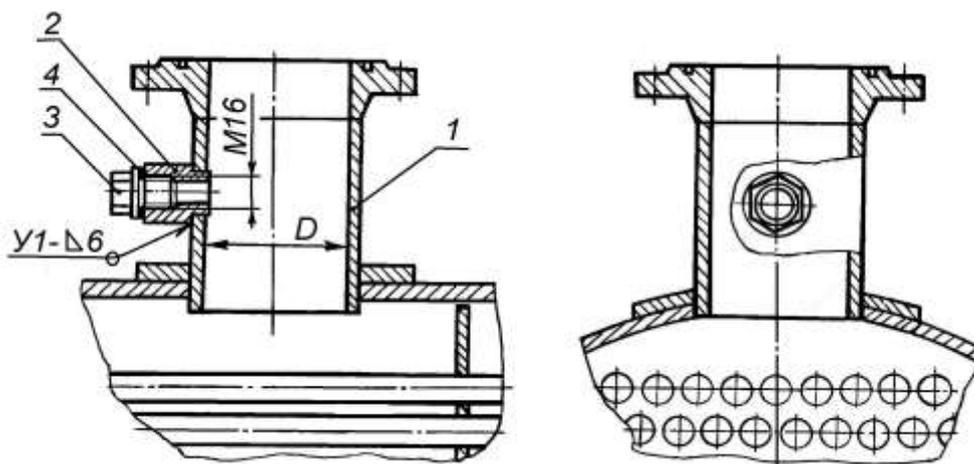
Штуцер с пробкой для спуска воздуха (воздушник) из межтрубного пространства горизонтального теплообменника: 1 – патрубок с фланцем; 2 – приварная бобышка с метрической резьбой М16; 3 – пробка; 4 – прокладка
